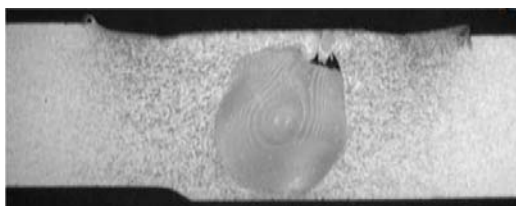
Пустота со стороны набегания сварного шва[3]
